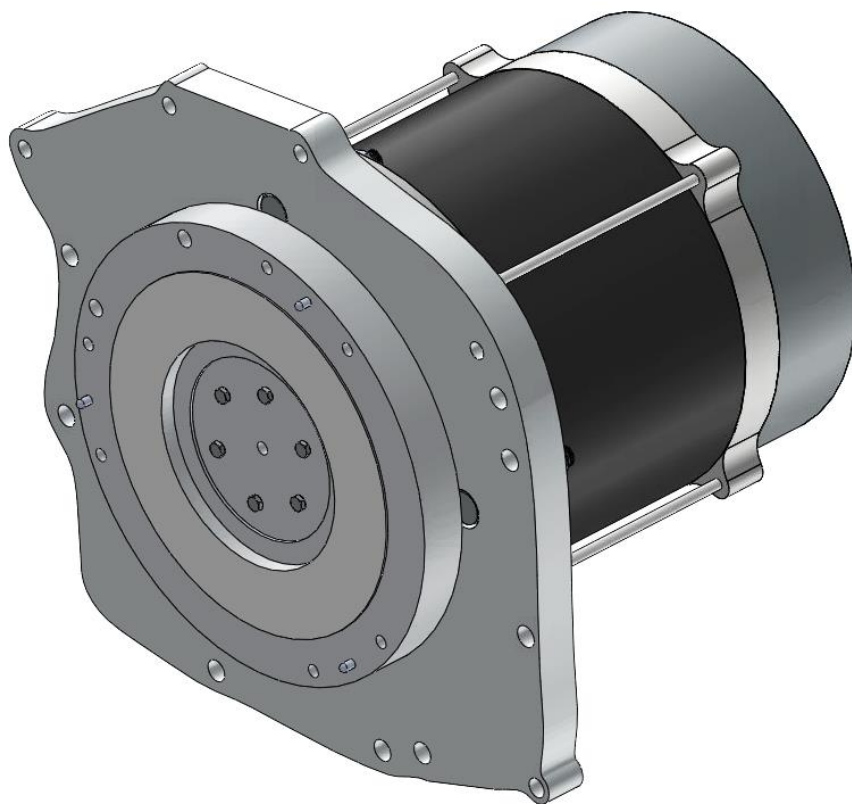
Vista del conjunt format per l'útil de fixació, el volant d'inèrcia, la placa adaptadora i el motor.
